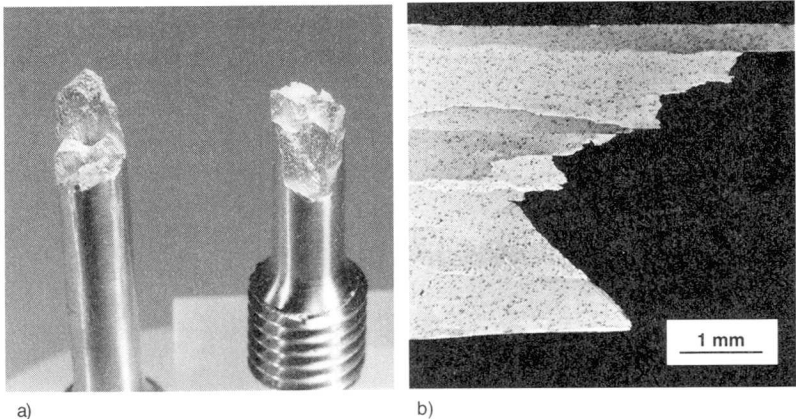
Zugprobe P240-T6; a) Makroaufnahme der Bruchfläche; b) Längsschliff
